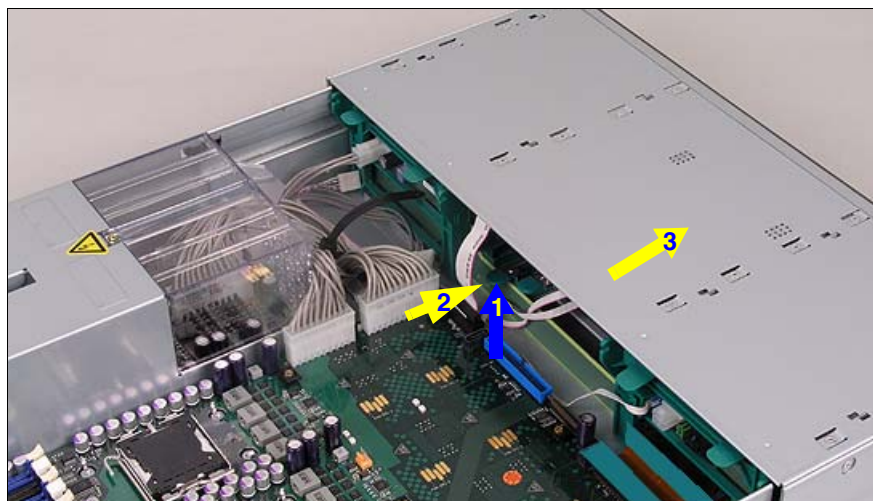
Entriegeln FD-Laufwerksmodul (zur besseren Sicht wurde die Lüfterbox entfernt)
